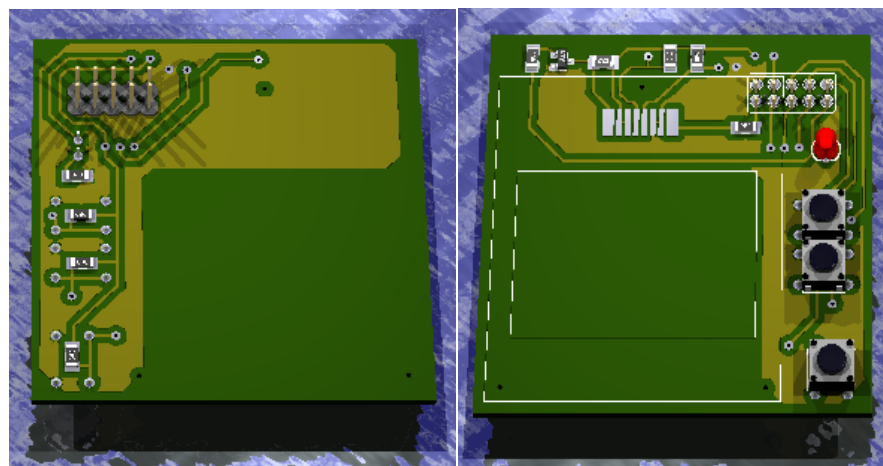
, PCB de la interfaz del CT01 en 3D. a) Bottom. b) Top.
